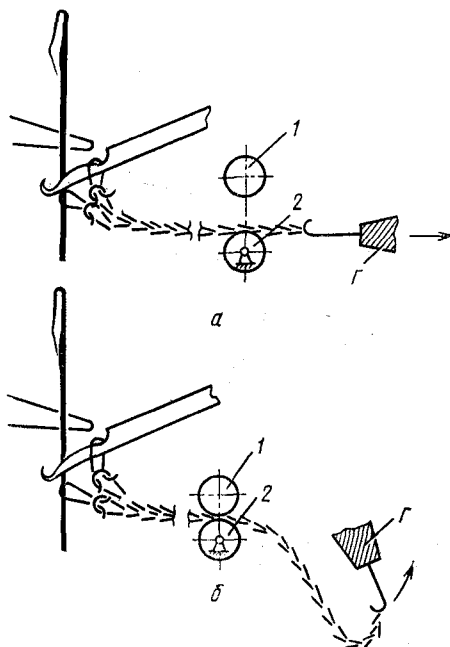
Схема оттяжки детали изделия рифлеными валиками
